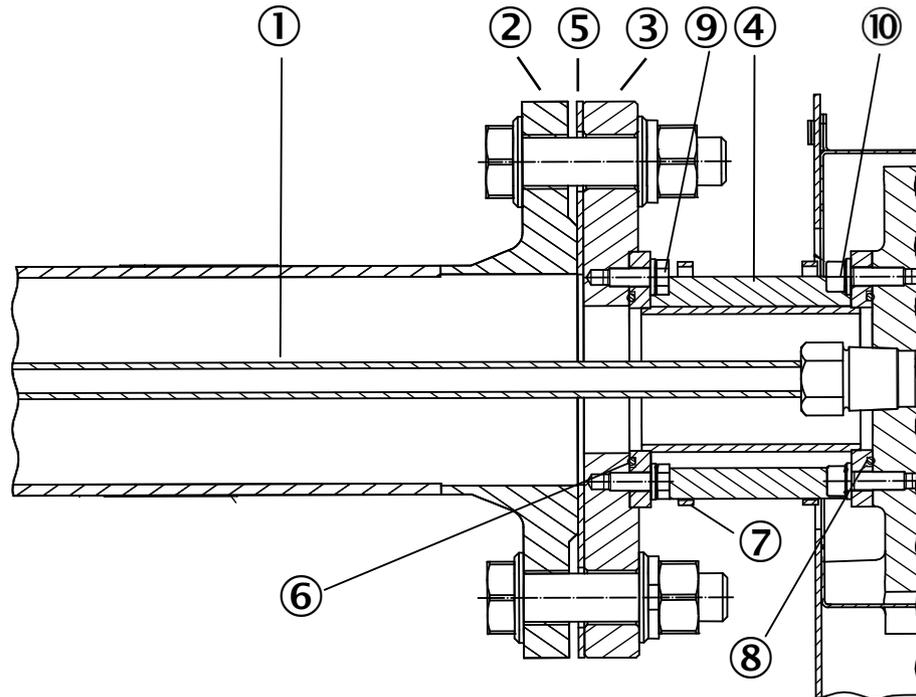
Vue détaillée du tube de sonde non chauffé
